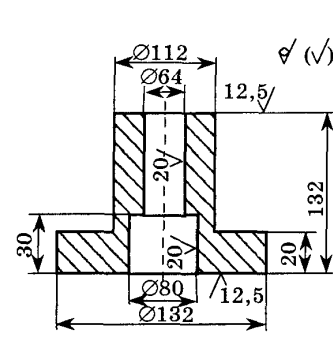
Чертеж детали: материал — сталь 45Л; класс точности размеров 9; ряд припусков 4
